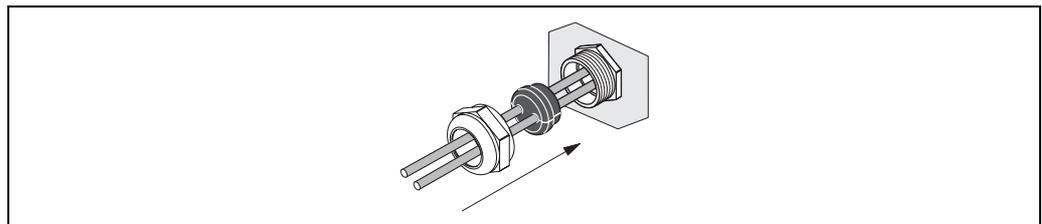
Pressacavo per due cavi di collegamento (2 × Ø 4 mm / 0.16") per ingresso cavo
